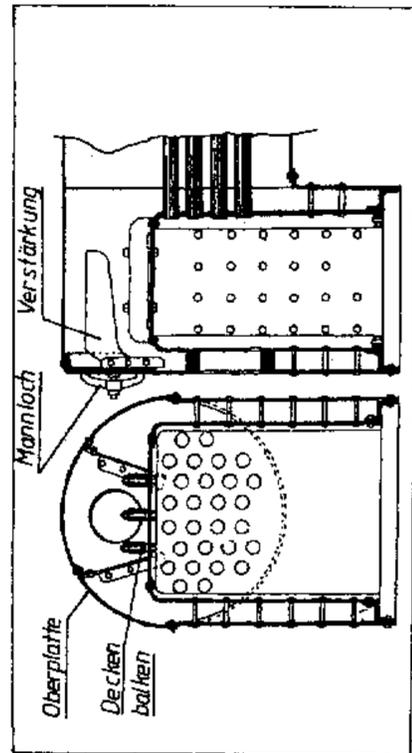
/1: Feuerbüchsenmantel mit halbzylindrischer Oberplatte und kastenförmiger, innerer Feuerbüchse
